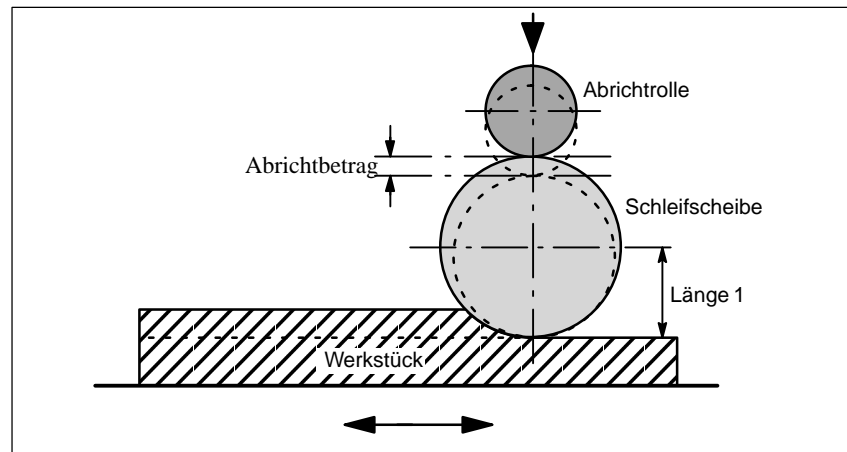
Abrichten während der Bearbeitung mit einer Abrichtrolle
